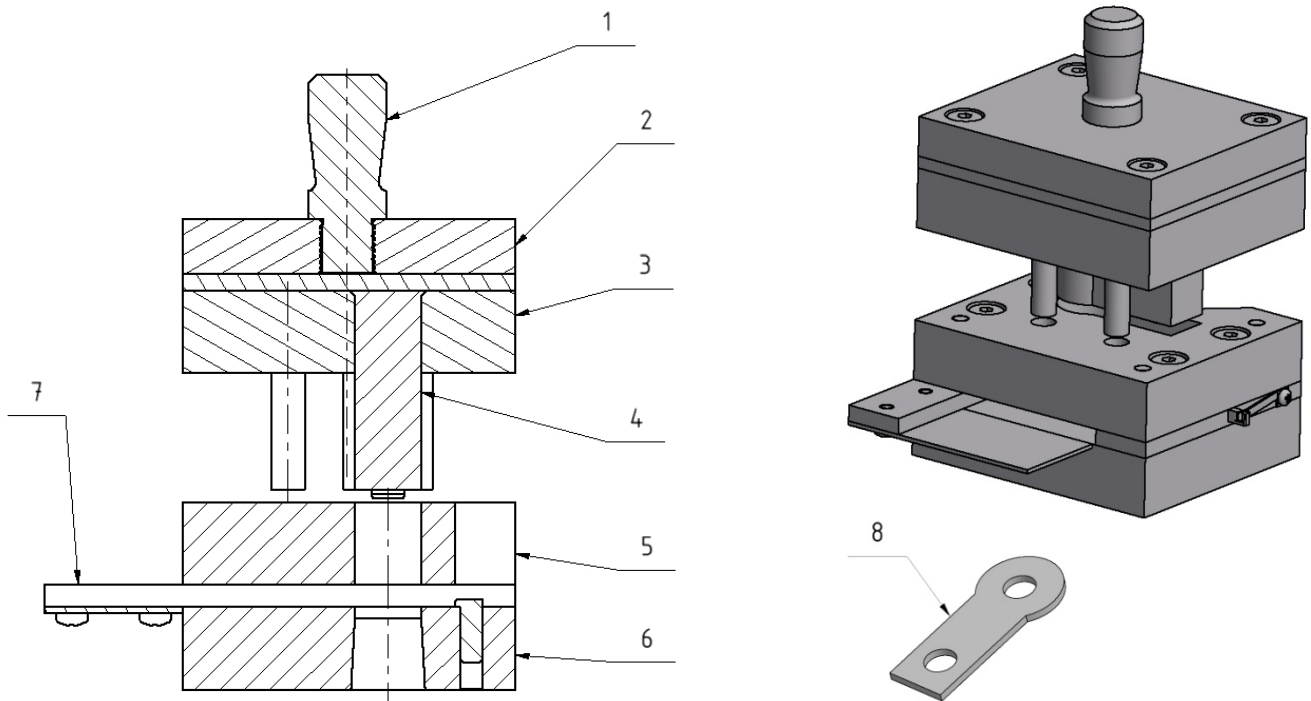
Folgeschneidwerkzeug für Platte mit zwei Bohrungen
